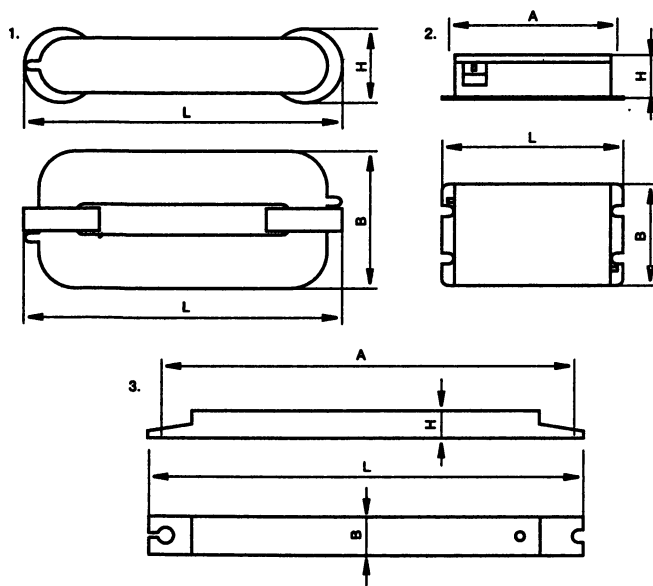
Габаритные размеры ламп ENDURA\
